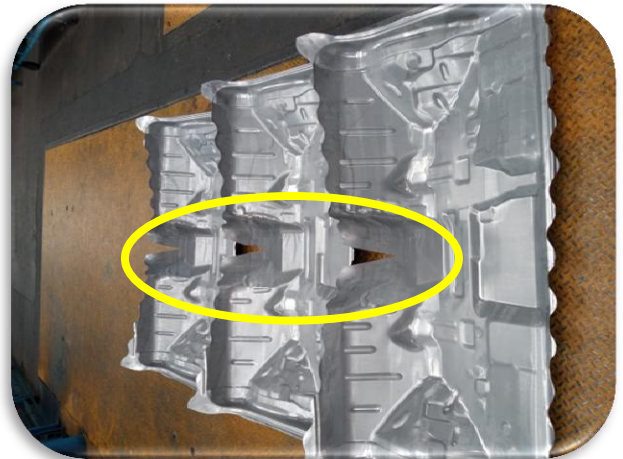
Pruebas de estampado con fractura, piezas múltiples
